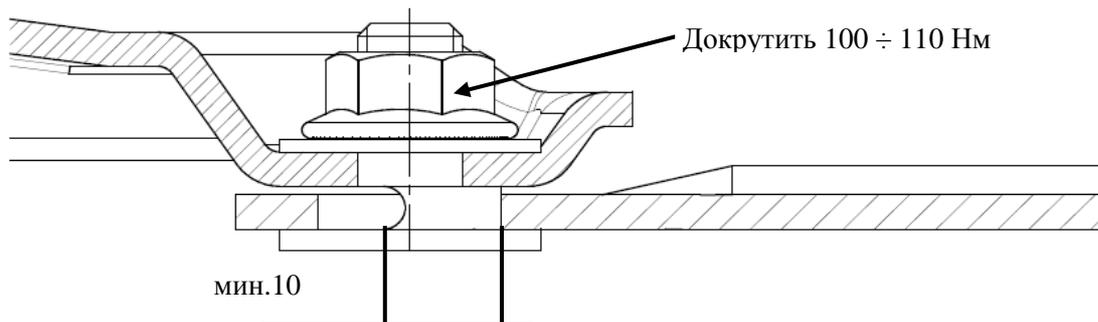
Допускаемый износ стержня держателя ножа
